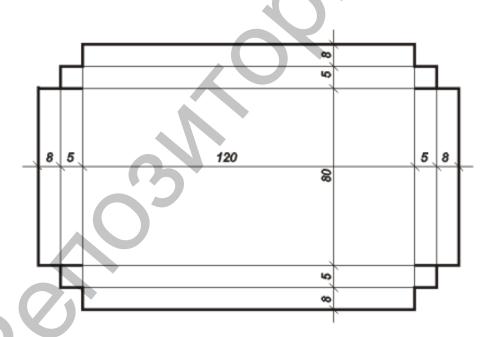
Чертеж подмакетника с рельефной поверхностью
